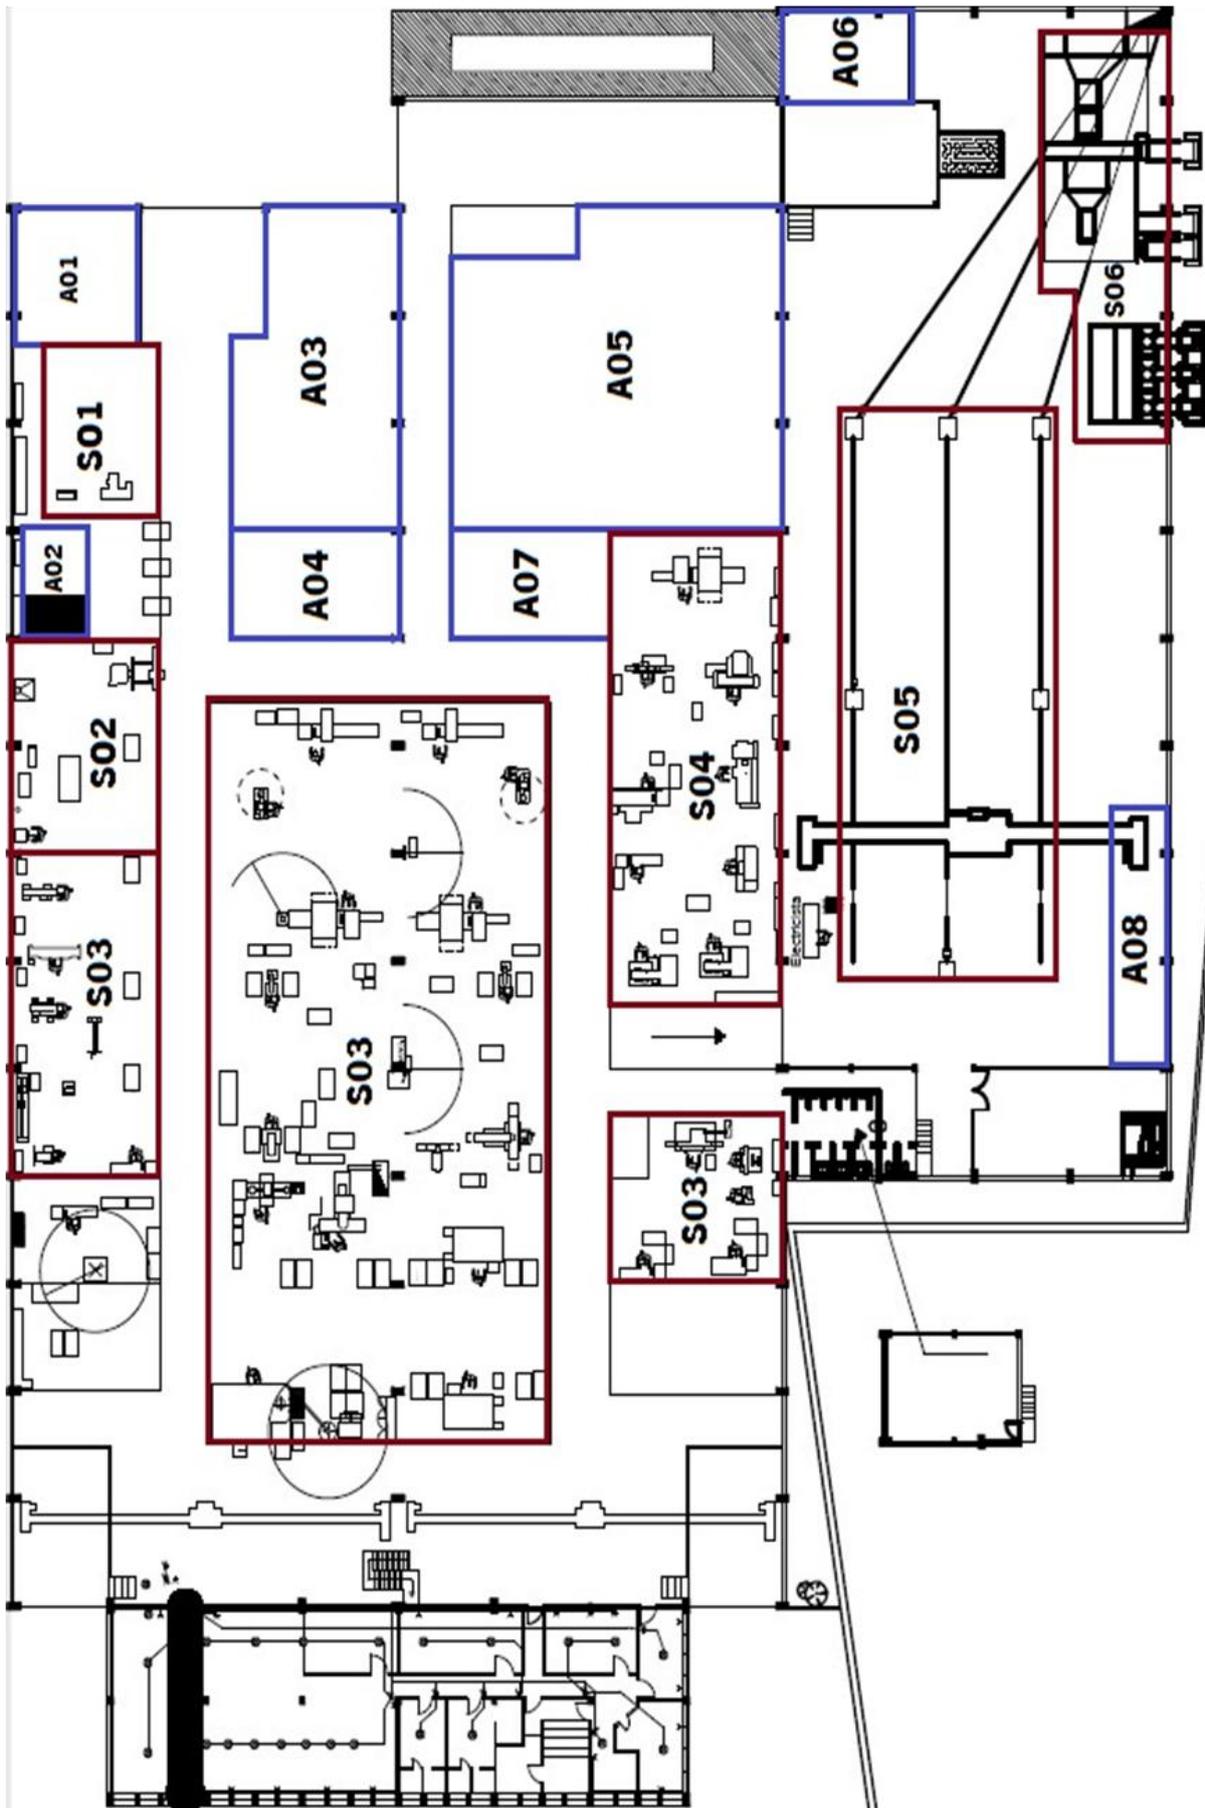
Layout com localização das zonas de armazenamento e secções de fabrico
